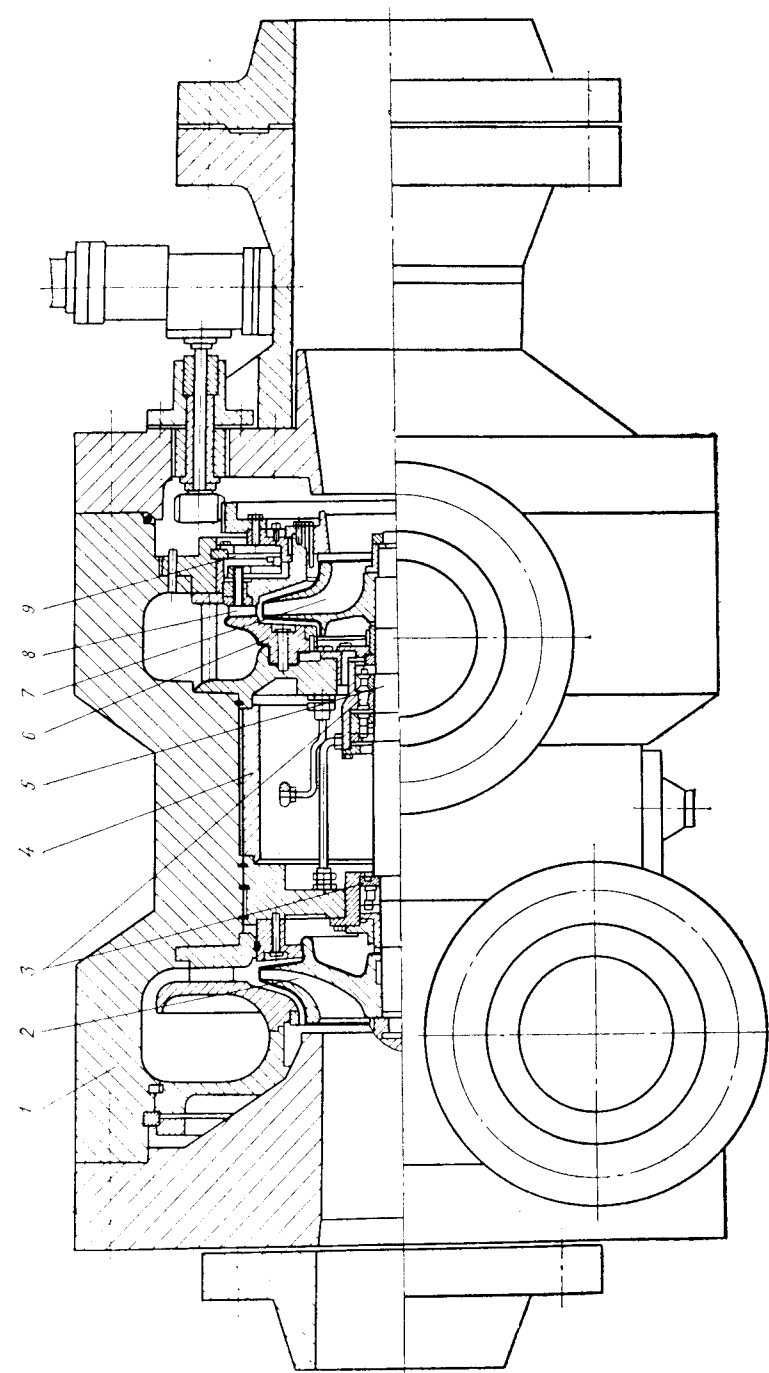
Схематичный разрез центростремительного турбодетандера и центробежного компрессора:
